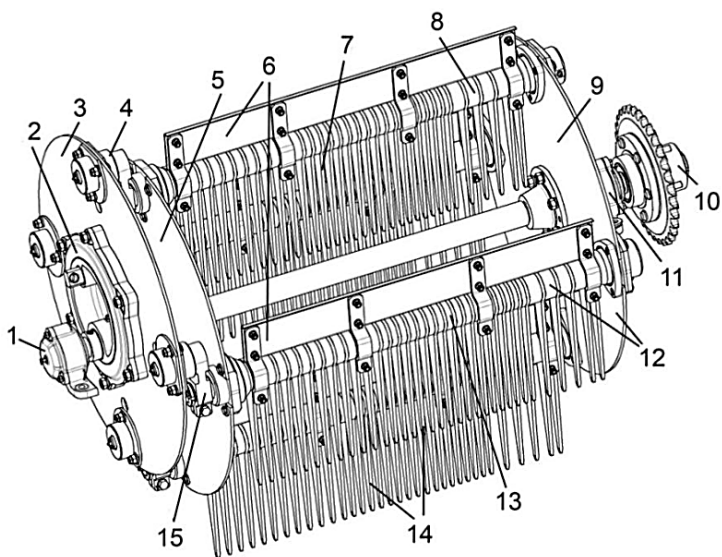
Очесывающий барабан: 1, 11 – корпуса; 2 – эксцентрик; 3 – эксцентриковый диск; 4, 15 – поводки; 5, 9 – диски очесывателя; 6 – лопатки; 7, 14 – зубья гребенок; 8, 13 – гребенки; 10 – обгонная муфта; 12 – очесыватель
